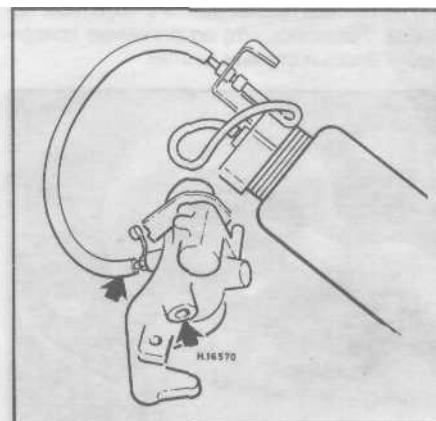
Заполнение суппорта тормозной жидкостью перед установкой. Стрелки указывают ниппель выпуска воздуха и место подсоединений тормозного шланга
